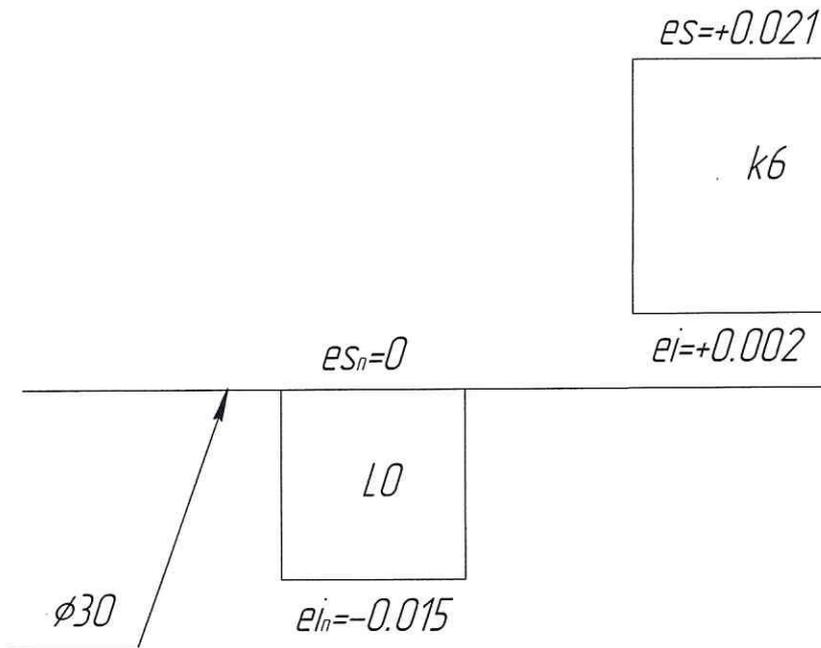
Схема расположения полей допусков деталей соединения
